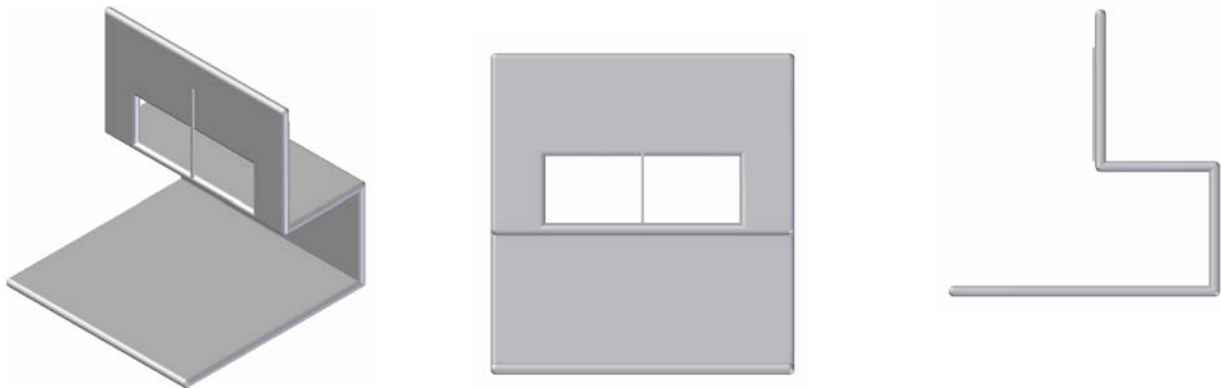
Posicionador metálico utilizado para inclusão dos dentes em resina acrílica.
